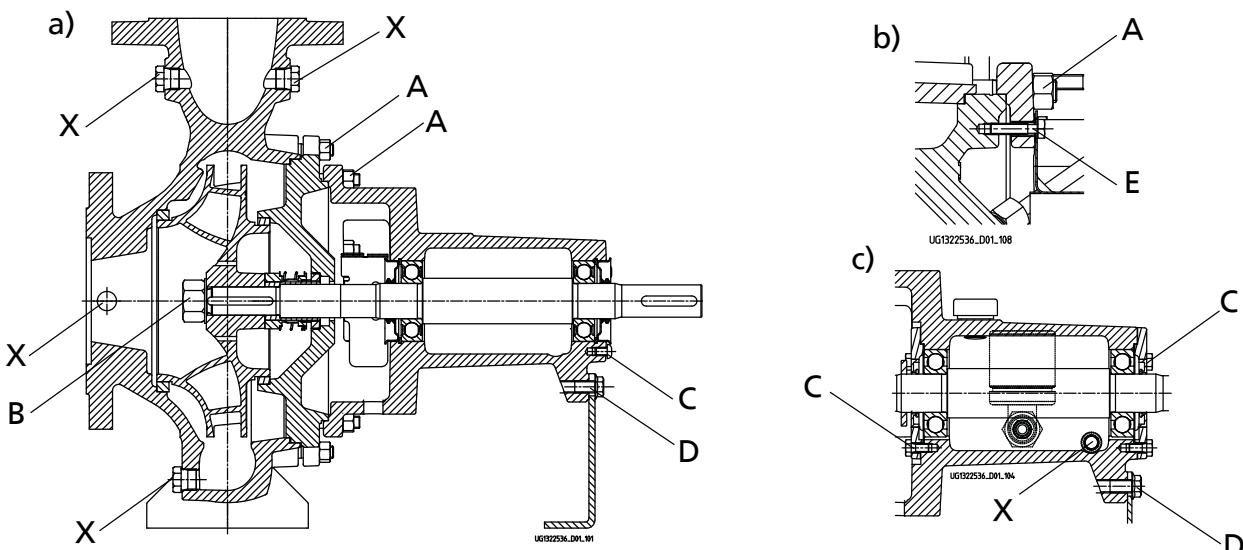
Места затяжки резьбовых соединений: исполнение с привинчивающей крышкой корпуса и пластичной смазкой (а), исполнение с зажимной крышкой корпуса (б) и жидкой смазкой (с)
